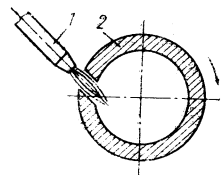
Принцип резки: 1 — резак для микролучевой резки РВ100; 2 — заготовка
